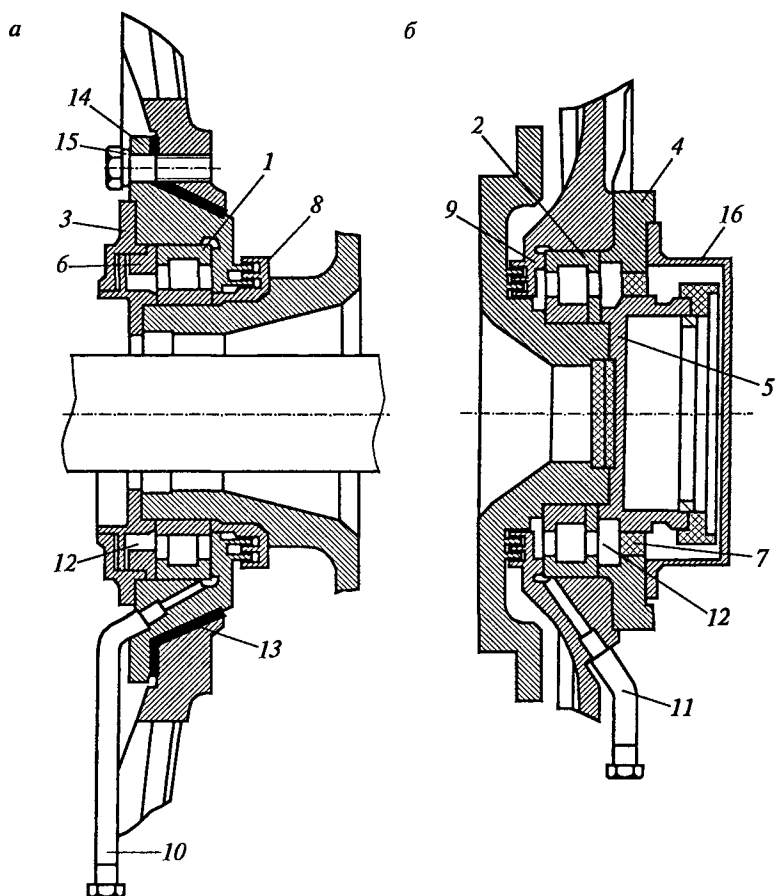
Система уплотнения подшипников и подвода смазки тягового электродвигателя НТА-1200:
